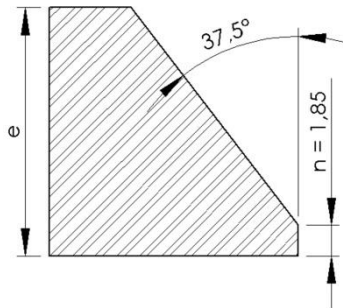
Chanfro tipo “V” utilizado por Chowdary [14] para a execução de um procedimento de soldagem TIG mecanizado. Dimensões em mm.
